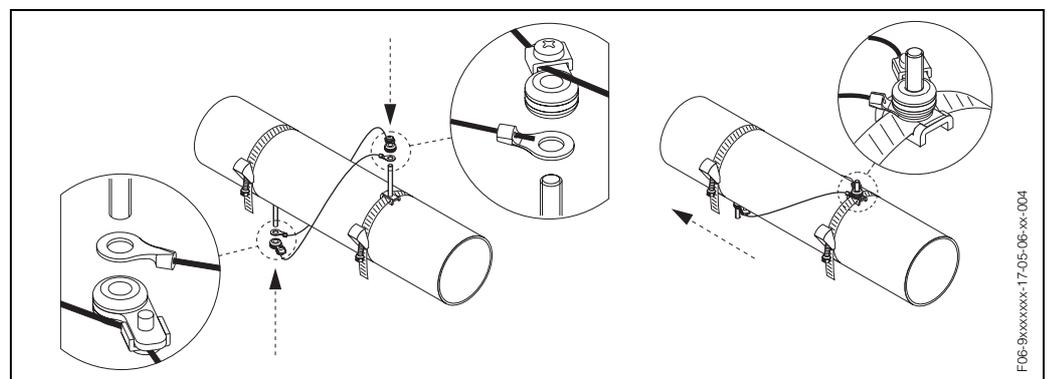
Utilización del equipo medidor de cables para colocar los pernos roscados en la posición apropiada
